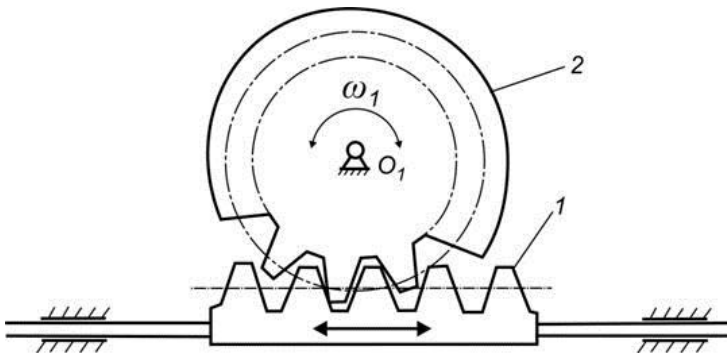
Зубчатый механизм с реечным зацеплением
